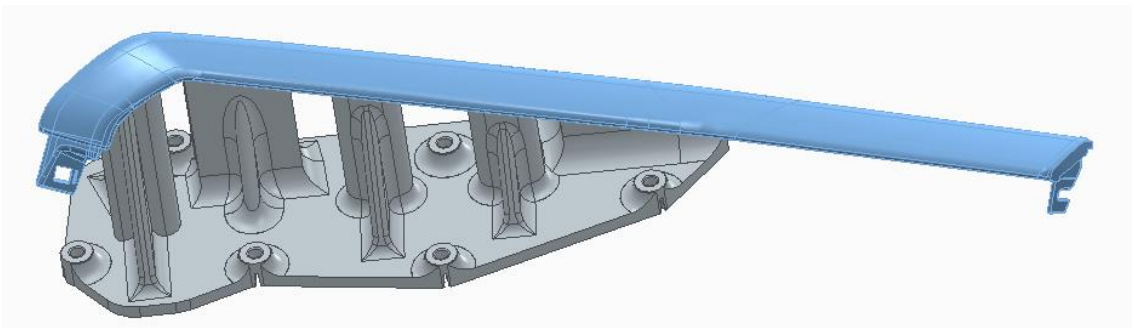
Módulo 2 del utillaje 2 con pieza de trabajo incorporada
